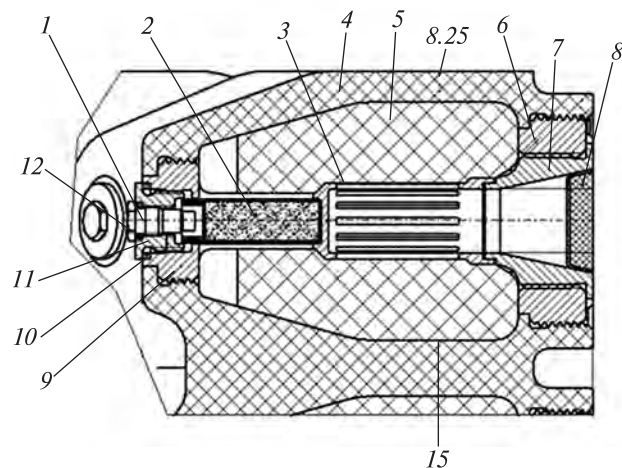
Конструкция импульсных твердотопливных ракетных двигателей: 1 — пиропатрон, 2 — воспламенитель, 3 — сетка, 4 — корпус, 5 — заряд, 6 — гайка, 7 — сопло, 8 — заглушка, 9 — диафрагма, 10 — уплотнительное кольцо, 11 — крышка, 12 — прокладка
